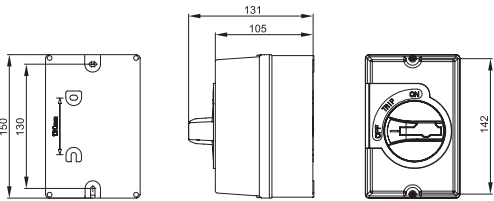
Габаритные и установочные размеры оболочки защитной / Figure 3 – Overall and mounting dimensions of the protective enclosure / 3 сурет – Қорғаныш қабықшасының габариттік және орнату өлшемдері
